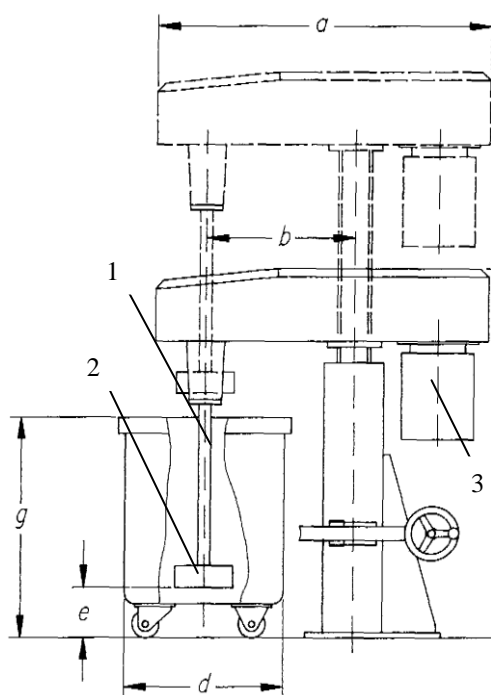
Схема диспергатора «Turbo» : 1 - вал; 2 - сетчатый ротор;
